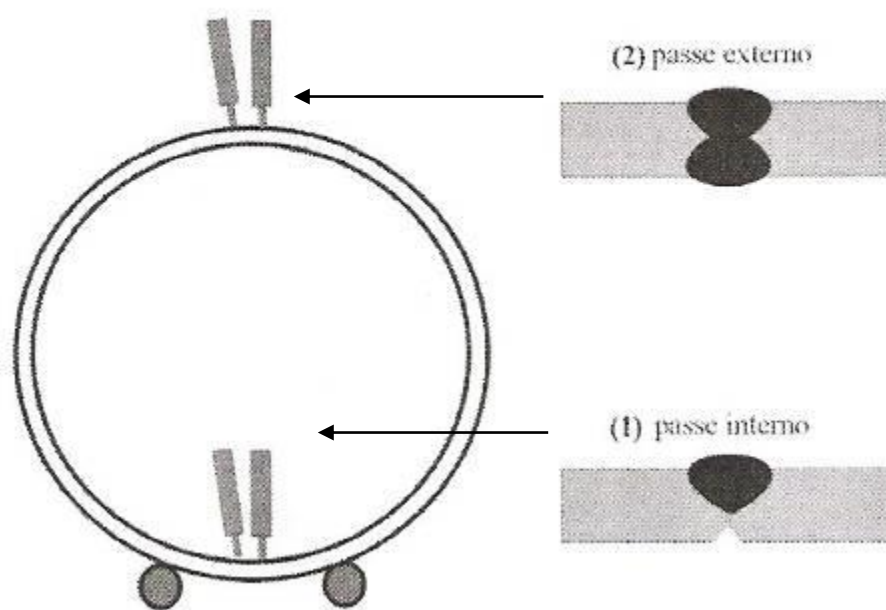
Configuração da soldagem a arco submerso na parte interna e externa utilizando dois arames [02].
